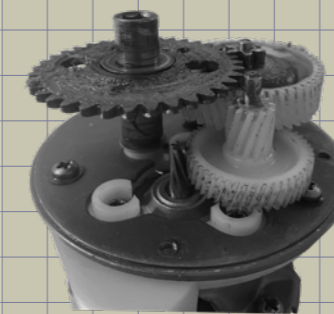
Train d'engrenages emmené par le pignon relié à l'axe du rotor.
